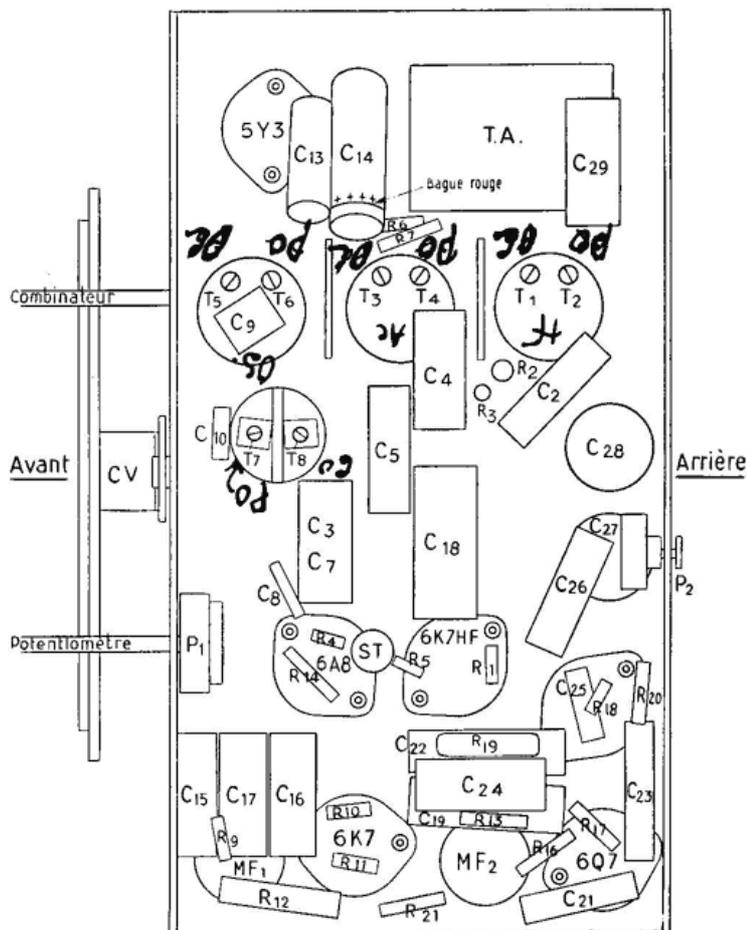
FIGURE IV : Le châssis du Récepteur Marconi 32 (vue du dessous)
